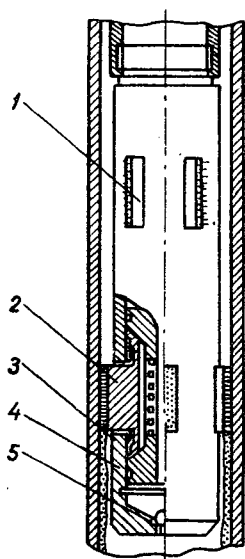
Гидравлическая щетка: 1-шпильки; 2-вкладыш; 3-поршень; 4-корпус; 5-обратный клапан.
